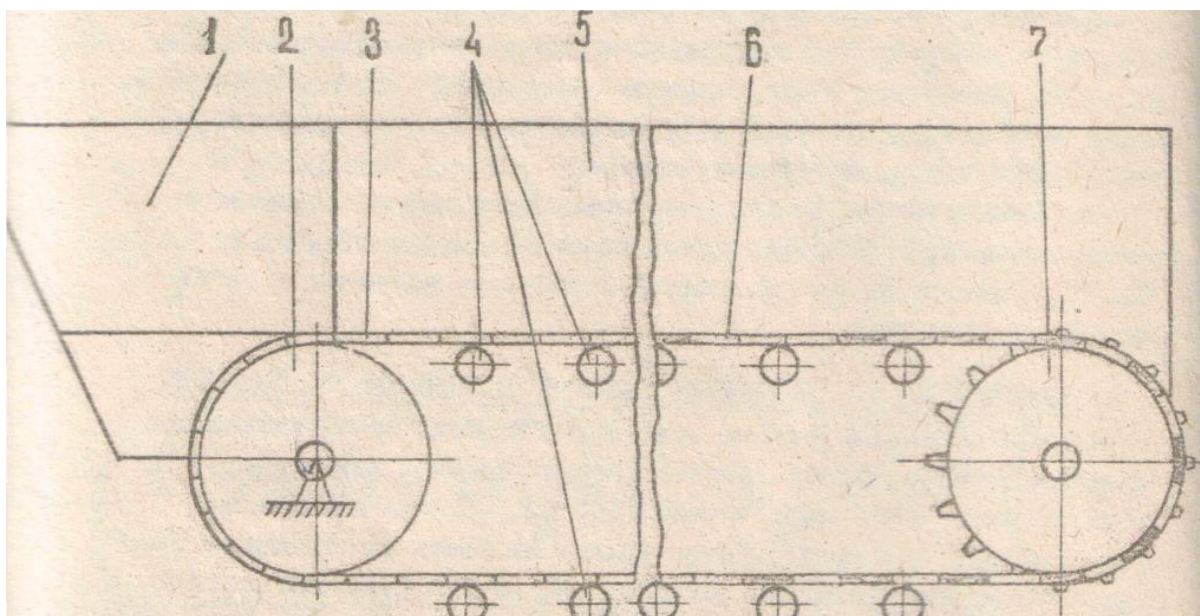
Схема транспортера ТВК-80Б: 1-загрузочный бункер; 2-натяжная станция; 3-прорезиненная лента; 4-поддерживающие ролики; 5-кормовой желоб; 6-цепь; 7-приводная станция.
